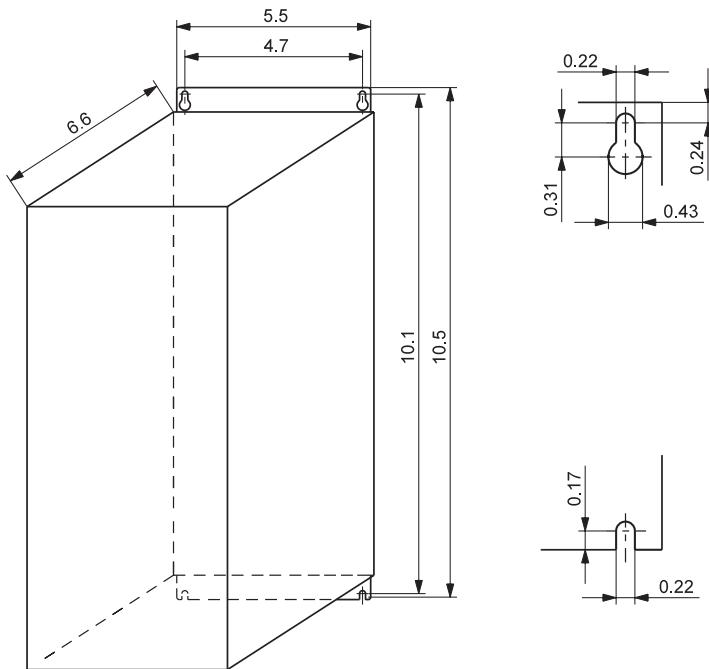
Croquis des dimensions du CU 321 (sans l'ensemble NEMA 1)
